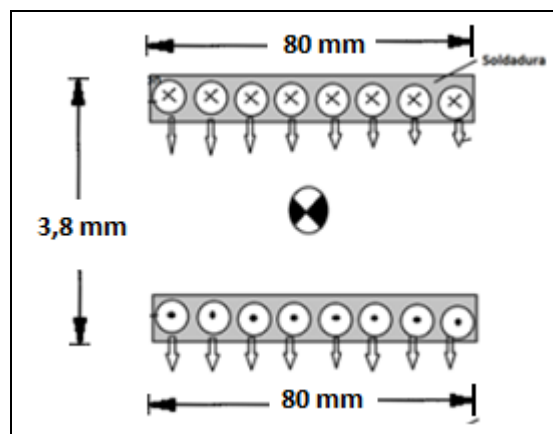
DIMENSIONAMIENTO DEL CORDÓN DE SOLDADURA EN LA VIGA.
